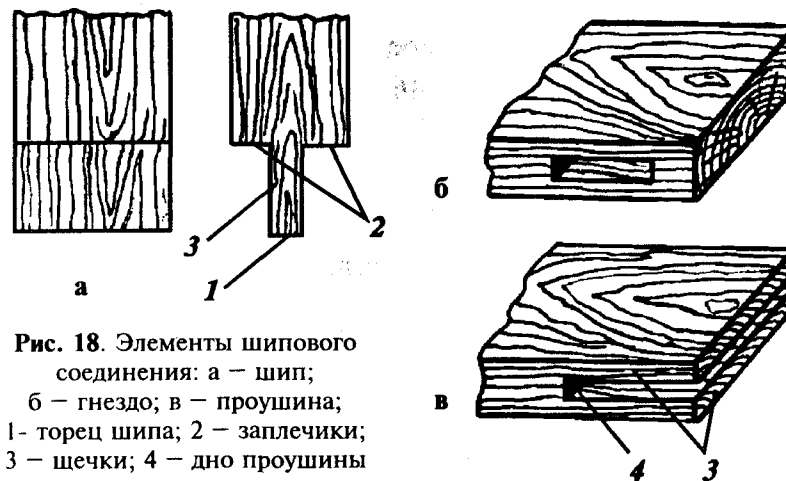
Элементы шипового соединения: а — шип; б — гнездо; в — проушина; 1 — торец шипа; 2 — заплечики; 3 — щечки; 4 — дно проушины
